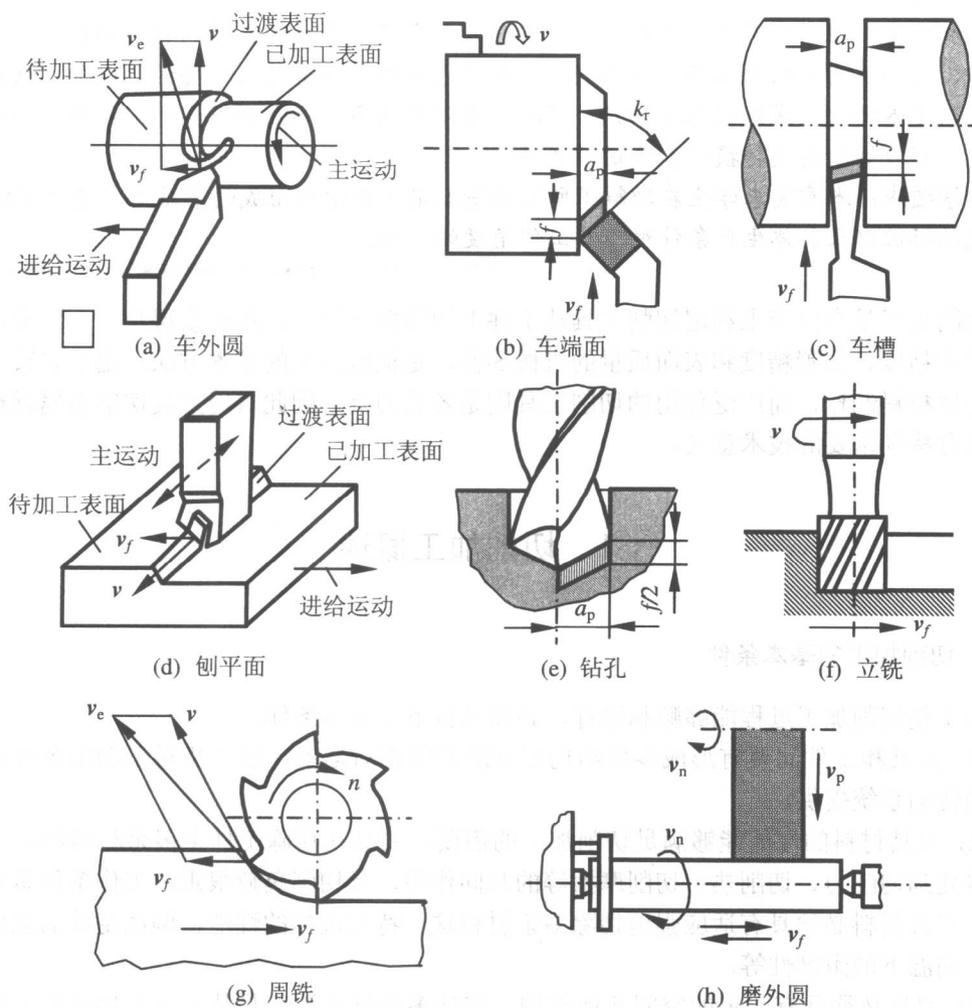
常见加工方法的加工表面、切削运动、切削用量
